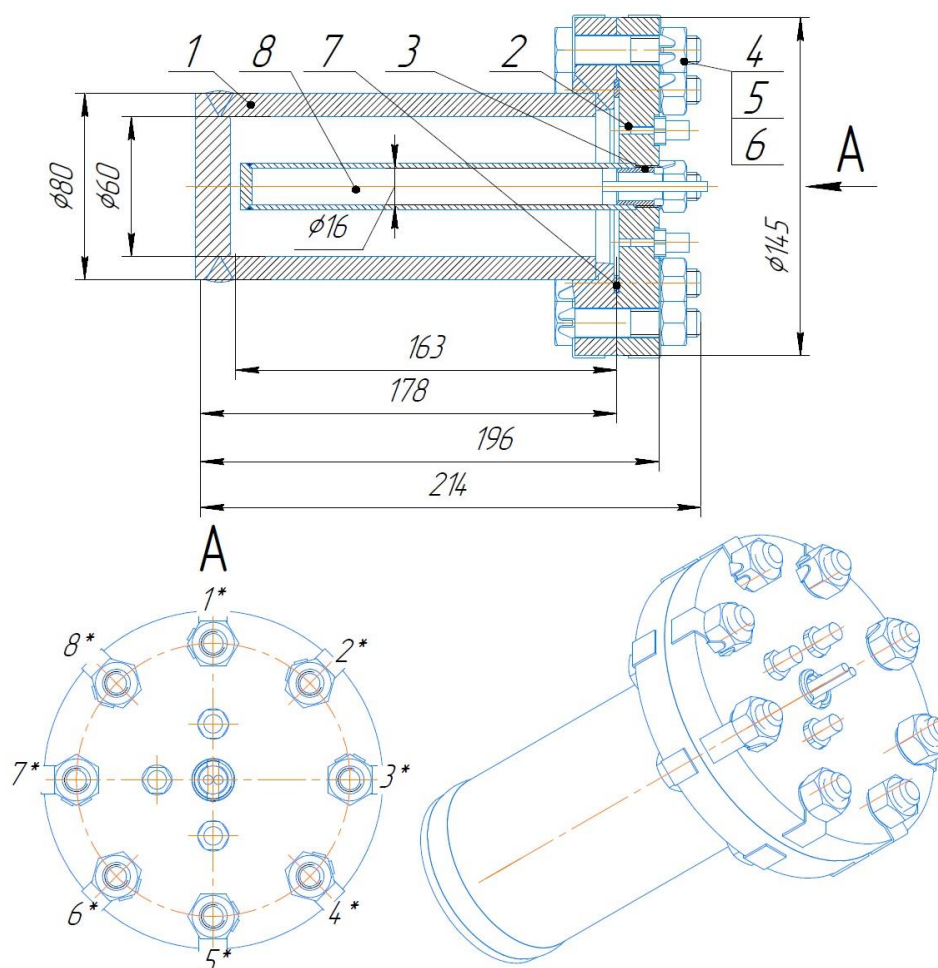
Схема испытательной ячейки для изучения металлгидридной системы с резистивным нагревателем: 1 – цилиндрический корпус; 2 – фланец; 3 – крепление резистивного нагревателя; 4 – болты М12; 5 – гайки М12; 6 – шайбы М12; 7 – медное уплотнительное кольцо; 8 – резистивный нагреватель.
